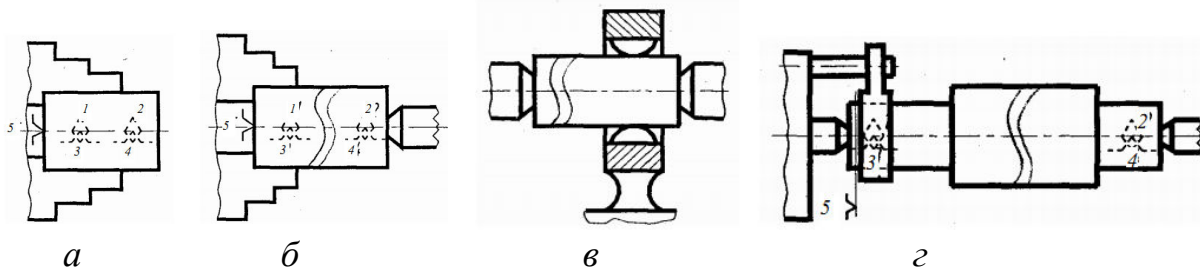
Установка вала: а - в патроні ($L/D < 4$);
